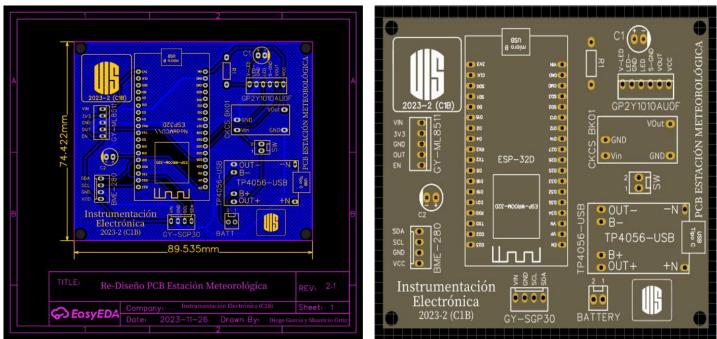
(a). Layout PCB en EasyEDA, (b). Modelo en 2D para la PCB en EasyEDA.
